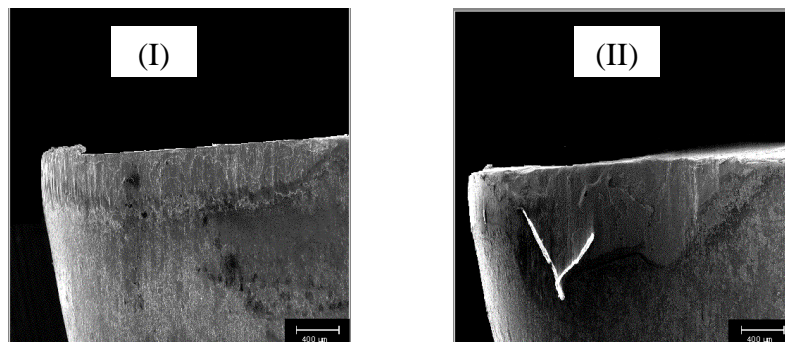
Desgaste de flanco na usinagem do VP20 (I) e VP20-UF (II) ($v_c = 123 \text{ m/min}$, $f_z = 0,141 \text{ mm/dente}$, $a_p = 1,7 \text{ mm}$).
